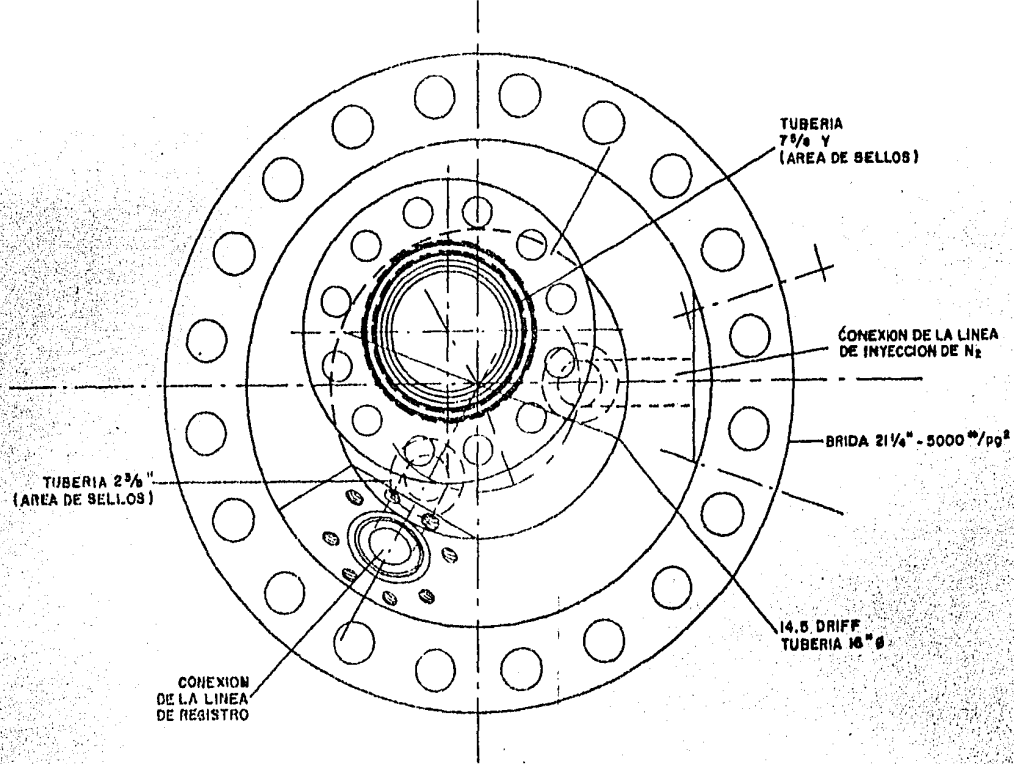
PLANTA DEL CARRETE DE INYECCION Y REGISTRO
